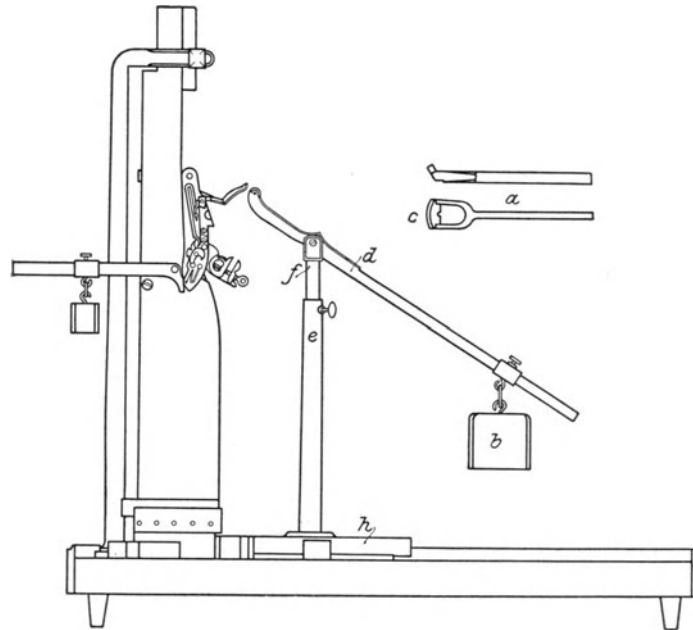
bis 17. Prüfmaschine für die Schloßfedern.
